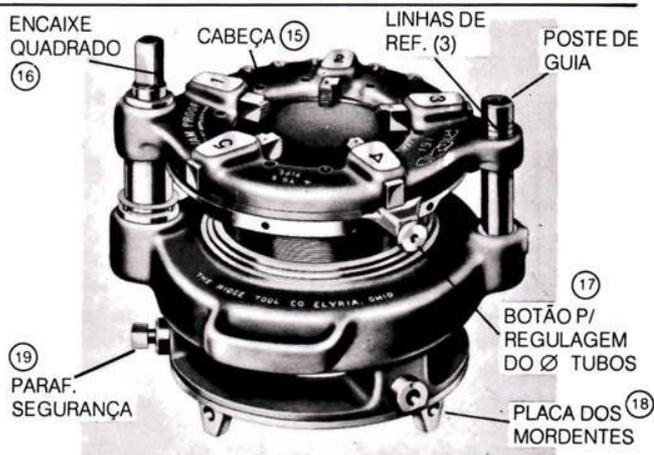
Montagem da tarraxa 161 com eixo universal 840
